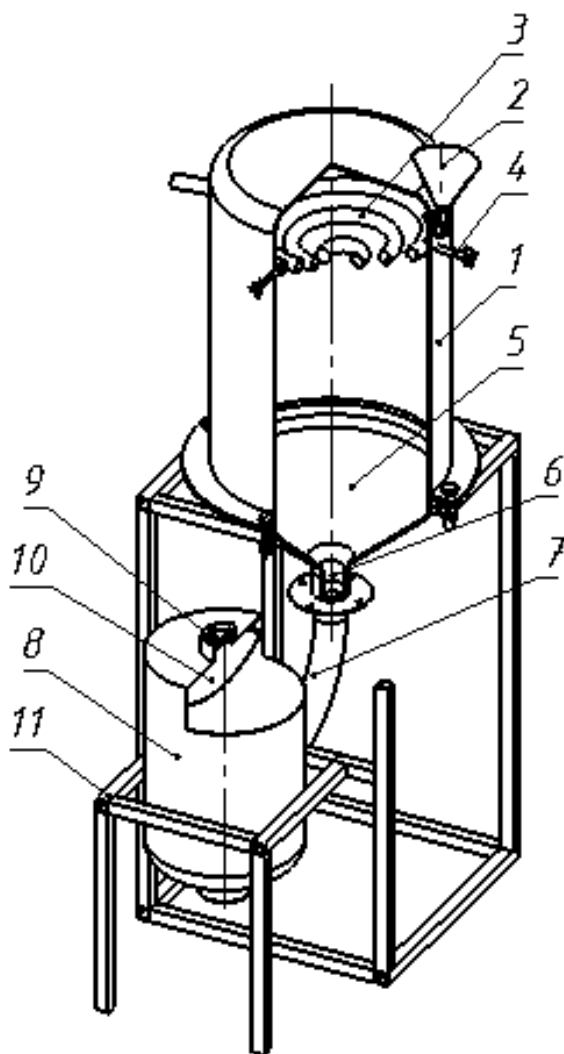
Пневматический смеситель со спиральной энергонесущей трубкой: 1 – камера; 2 – загрузочный патрубок; 3 – спиральная энергонесущая трубка; 4 – держатели; 5 – коническое днище; 6 – выгрузочный патрубок; 7 – труба; 8 – бункер; 9 – вентилятор; 10 – фильтр; 11 – рама
